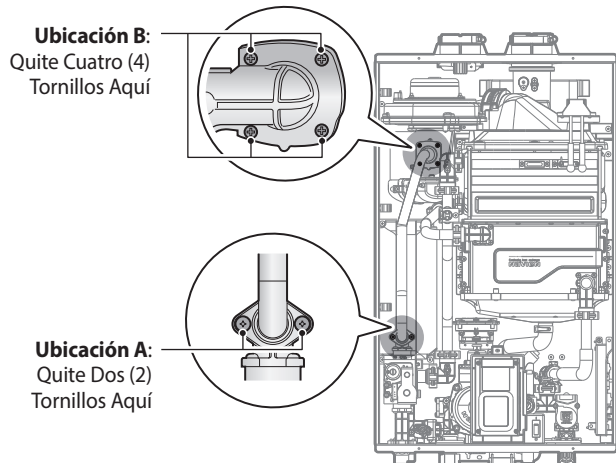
Separación de la Válvula de Gas del Tubo de Entrada de Gas y el Conjunto del Motor del Ventilador
